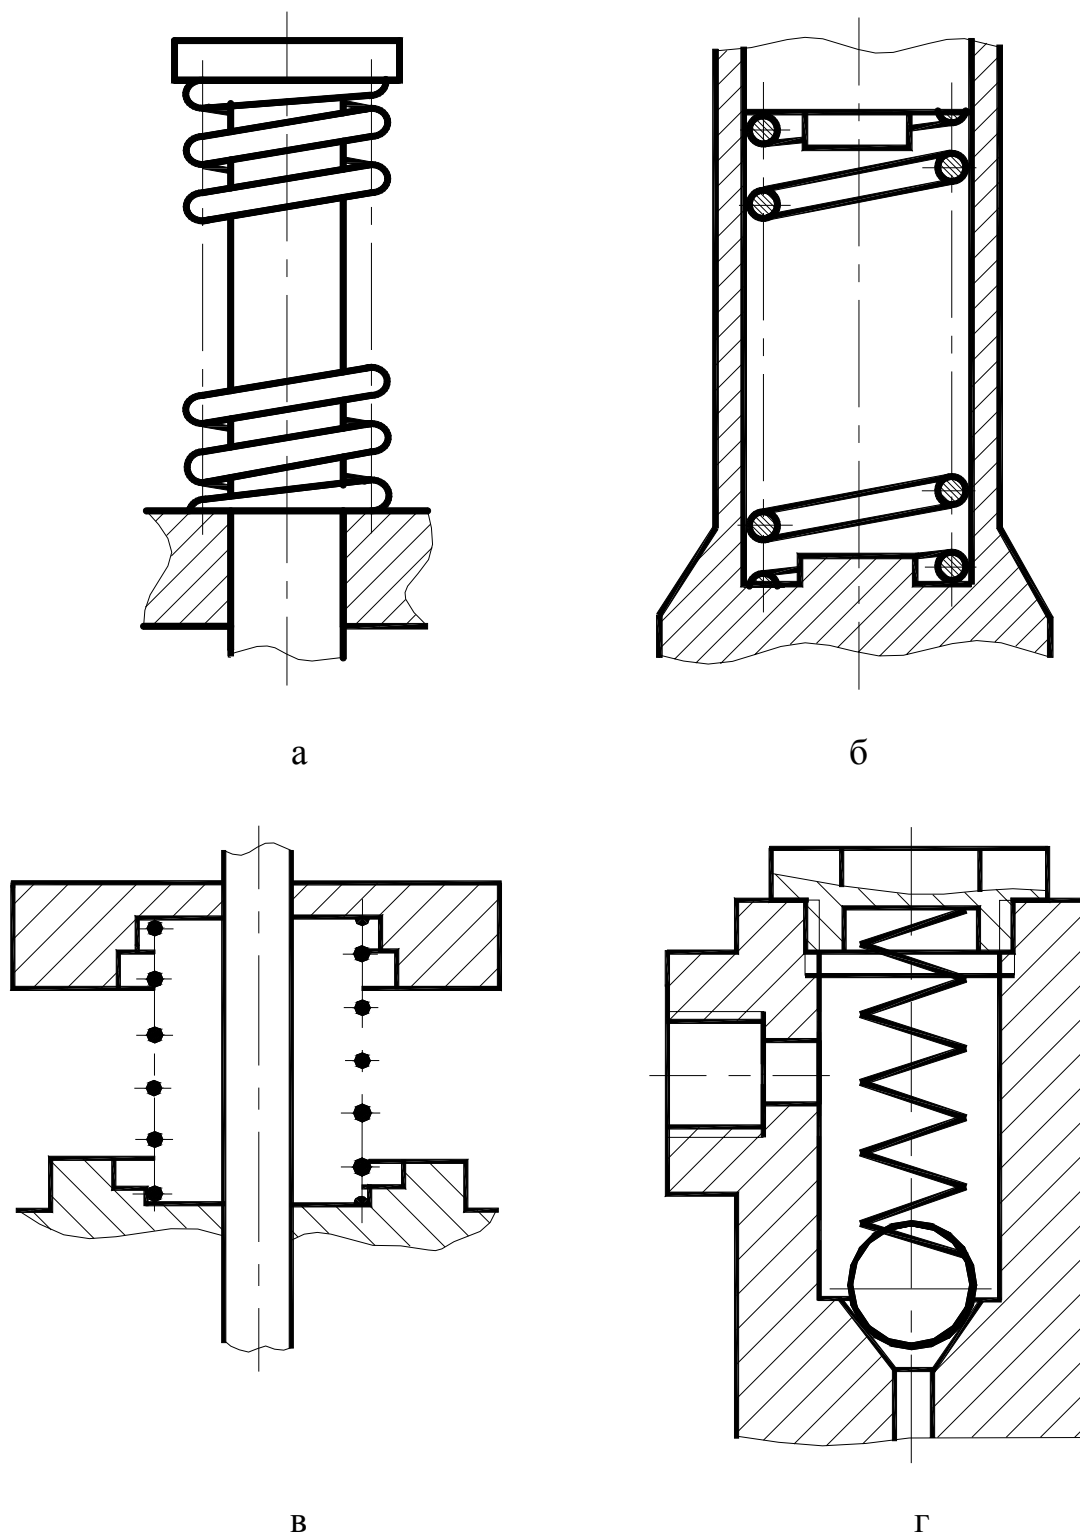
Способы изображения пружин на чертежах общего вида
